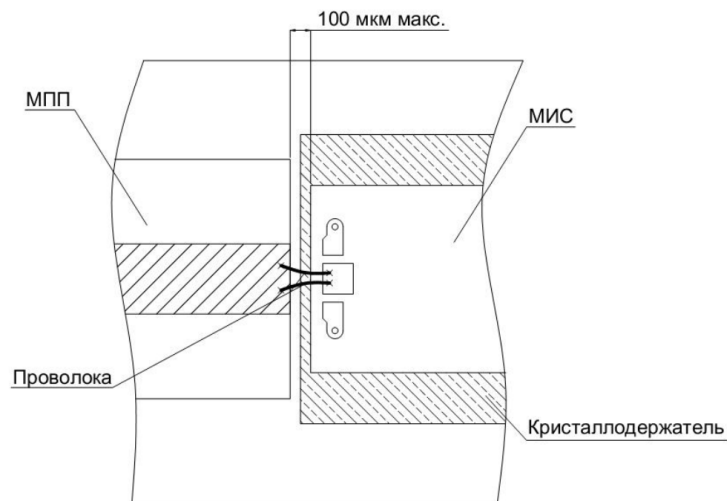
Габаритные и присоединительные размеры кристалла
